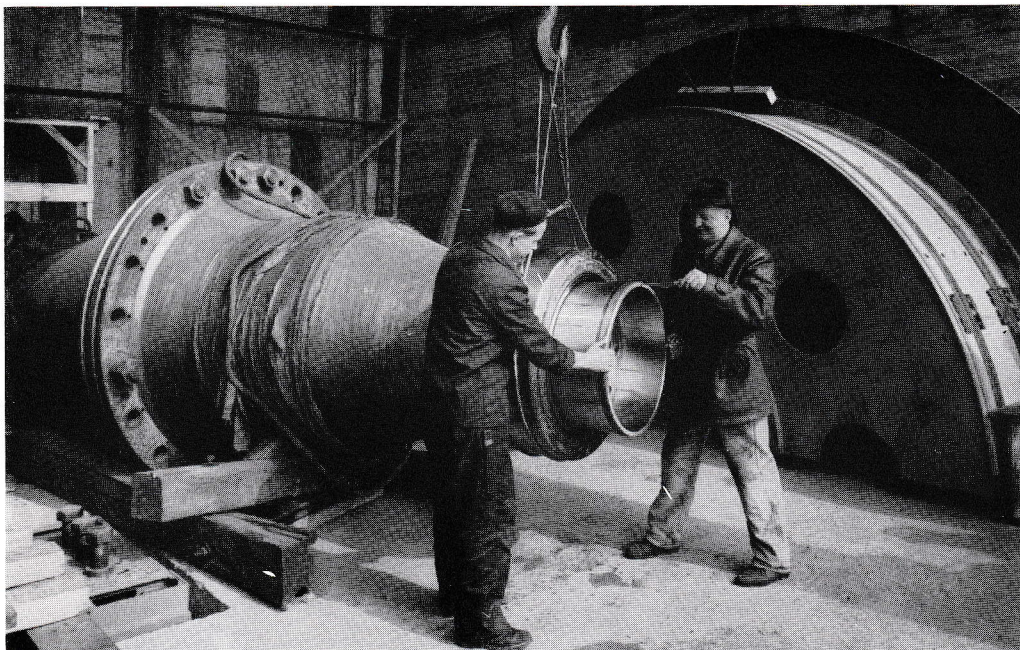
Montaje de uno de los rodamientos sobre el eje hueco del montacargas
